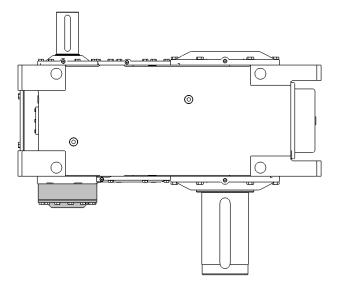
Промышленный редуктор с блокировкой обратного хода
